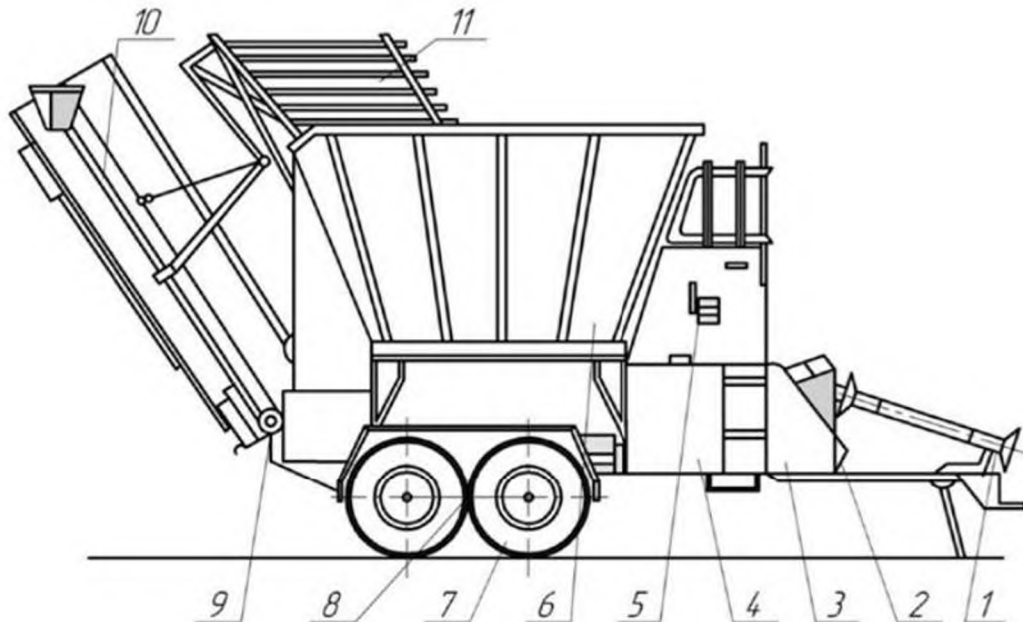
Дробарка-подрібнювач: 1 – вал; 2 – мультиплікатор; 3 – рама; 4 – гідравлічний привід; 5 – оглядова рампа; 6 – бункер; 7 – шасі; 8 – горизонтальний транспортер; 9 – пристрій для опускання; 10 – похилий транспортер; 11 – завантажувальний щит.
